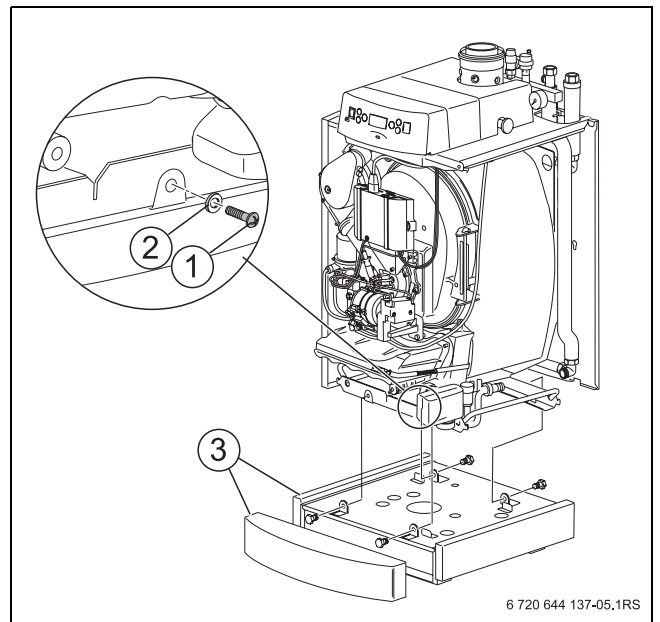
Montaggio della caldaia sul sottofondo per caldaia
